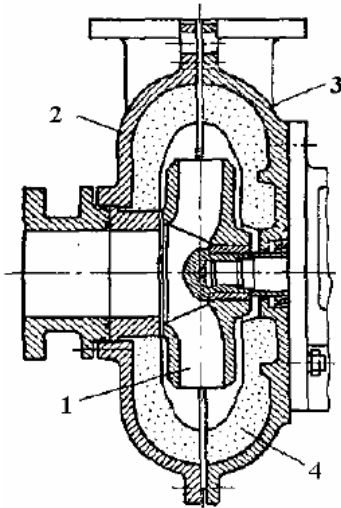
Однокорпусний ґрунтовий насос: 1 – робоче колесо; 2 – передня половина корпусу; 3 – задня половина корпусу; 4 – корундова футеровка
